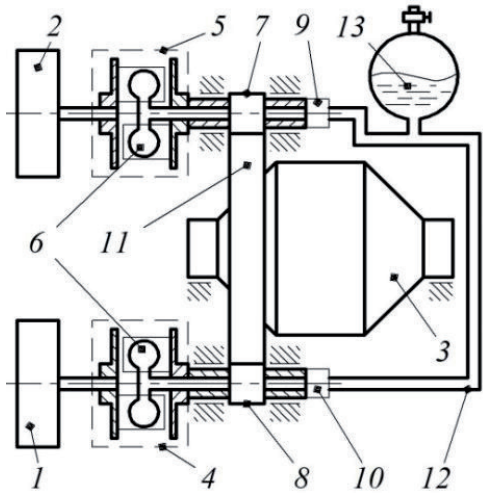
Схема двухдвигательного привода барабанной мельницы с муфтами, содержащими резинокордные оболочки: 1, 2 – синхронные двигатели; 3 – барабан мельницы; 4, 5 – упругие муфты, содержащие резинокордные оболочки; 6 – резинокордные оболочки; 7, 8 – приводные шестерни; 9, 10 – гидропневматические устройства; 11 – венцовая шестерня барабана; 12 – магистральный трубопровод; 13 – гидропневматический аккумулятор
